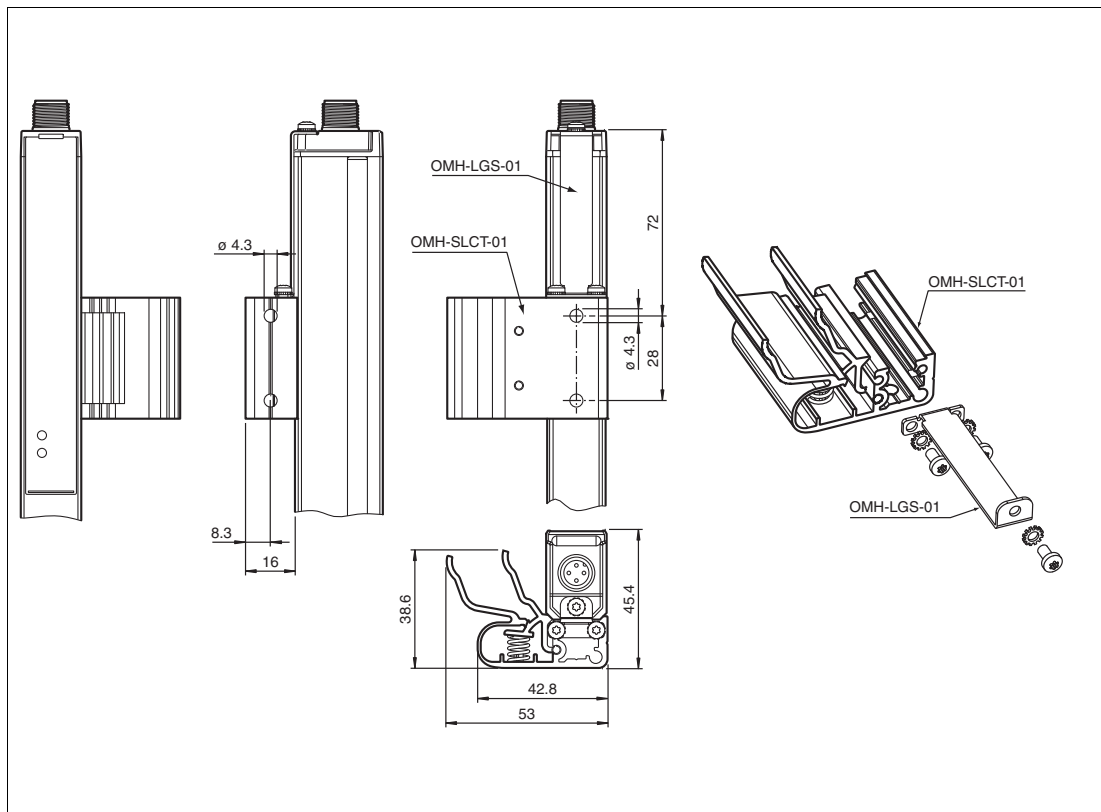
Abmessungszeichnung und Montage der Montagehilfe OMH-LGS-01
